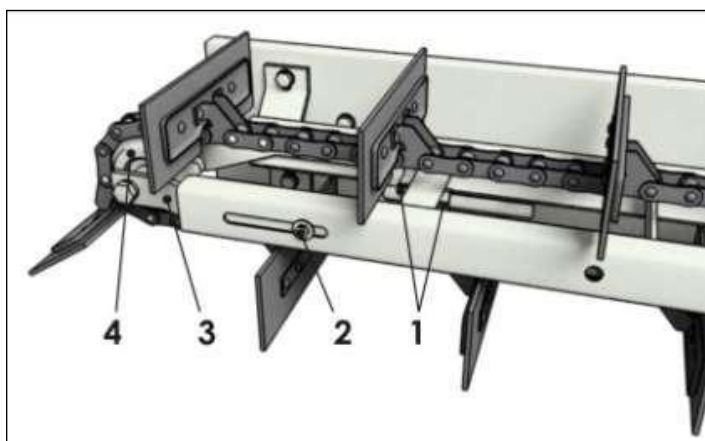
Регулировка натяжения скребковой цепи питателя 1 – Гайка; 2 – Болт; 3 – Натяжное устройство; 4 – Звездочка натяжная
